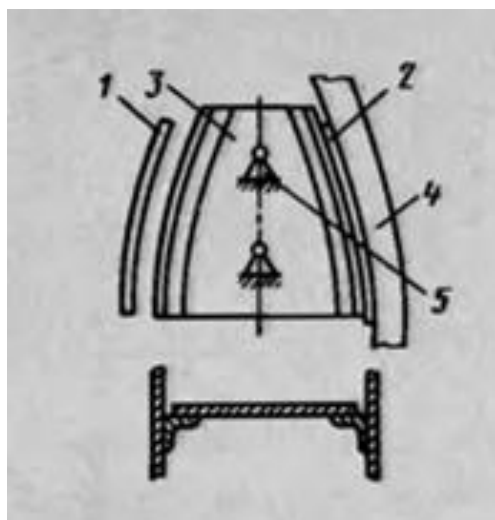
Схема сборки по базе «поверхность каркаса»:
